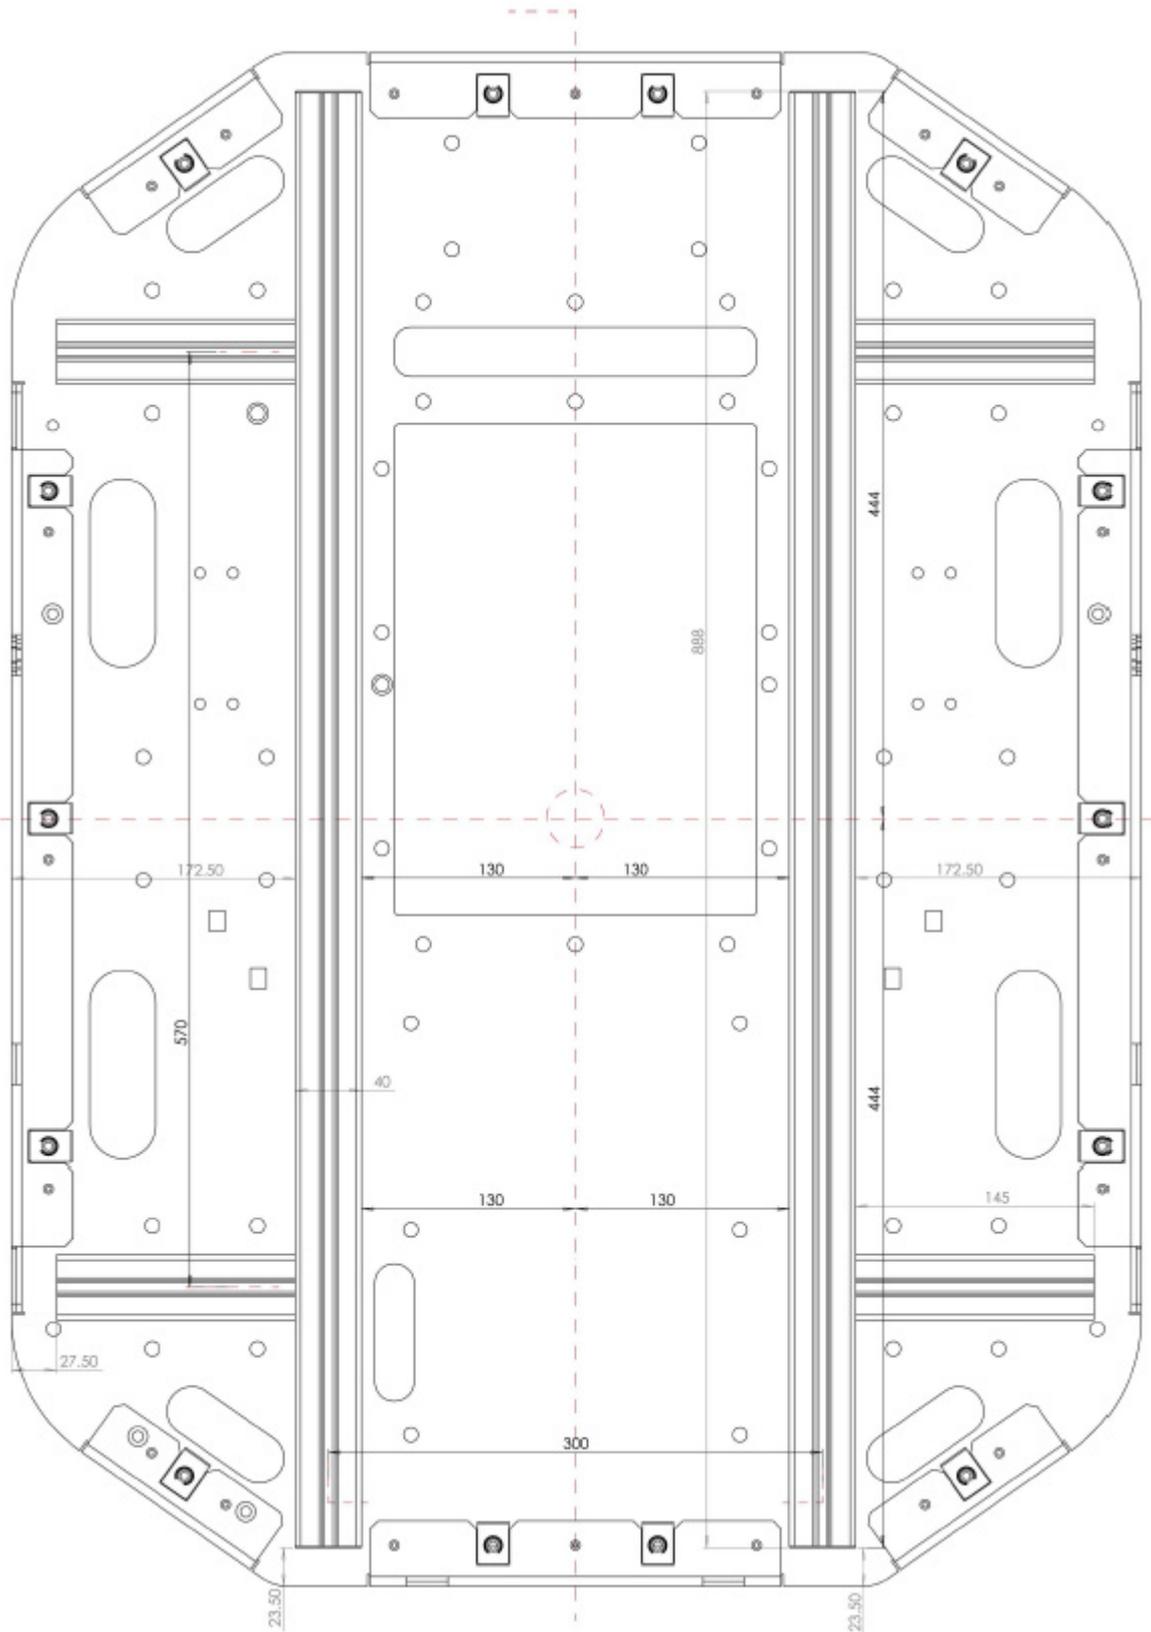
Emplacement des extrusions d'écrou en T sur la plaque supérieure
